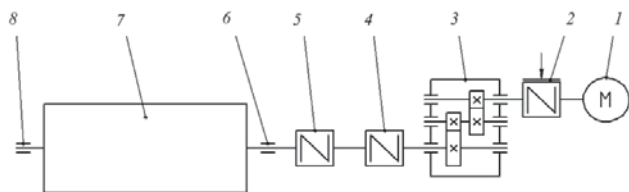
Кинематическая схема шаровой мельницы СММ2061 до реинжиниринга: 1 – электродвигатель; 2 – муфта с тормозом; 3 – редуктор; 4, 5 – муфты зубчатые; 6, 8 – подшипниковые узлы; 7 – мельница
